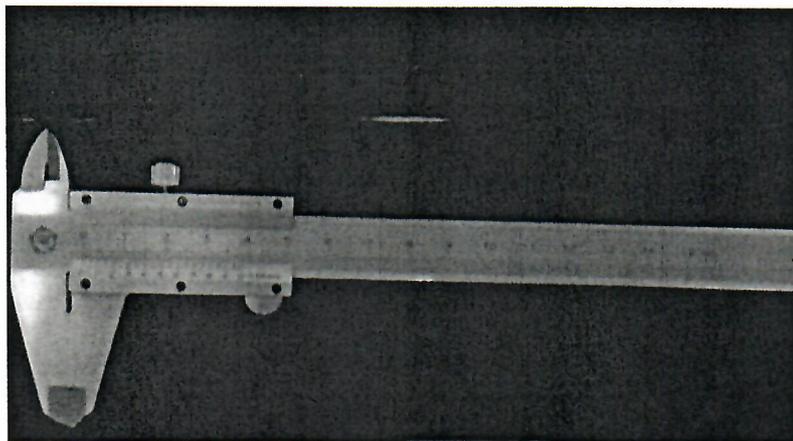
Общий вид штангенциркулей типа ШЦ-I.
